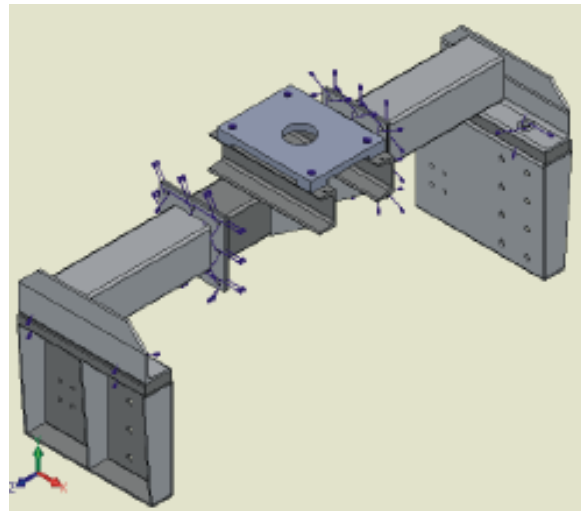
Modelo do elevador sem casa de máquinas [79]
